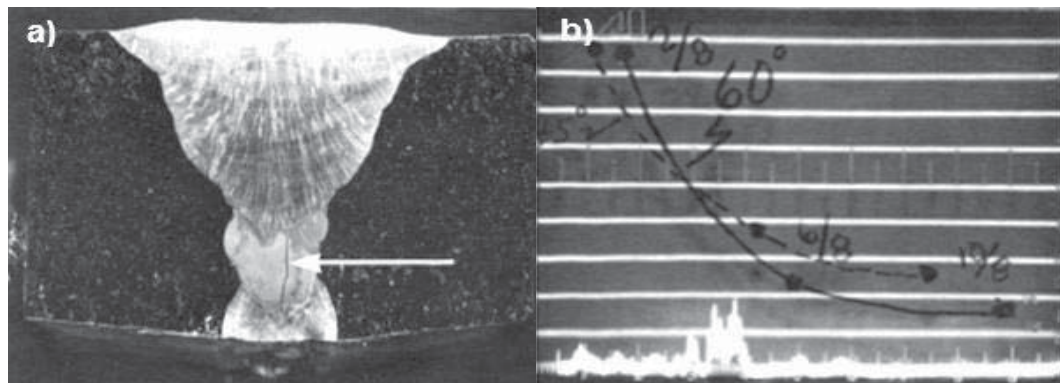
a) Configuración típica de una grieta dentro de la soldadura en el material de aporte, b) forma de la señal en A-Scan de una grieta.
